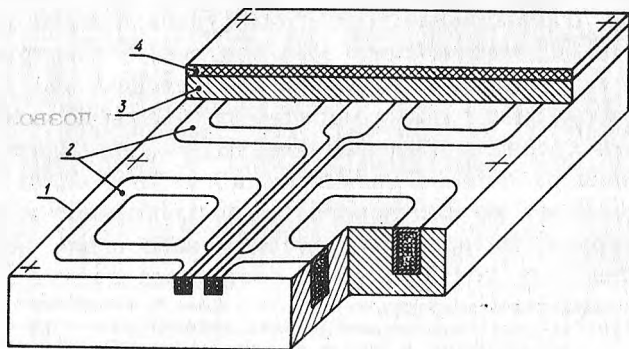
Нагревательный элемент: 1 - корпус; 2 - индукционные катушки; 3 - крышка корпуса; 4 - теплоизолятор.
